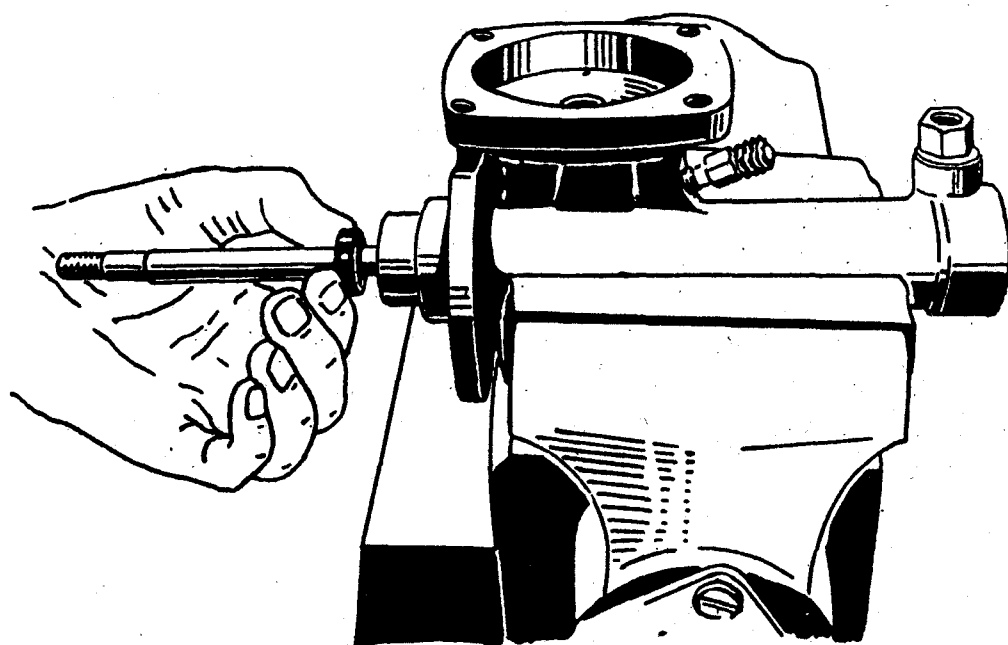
Установка вторичной манжеты в корпус уплотнителей
